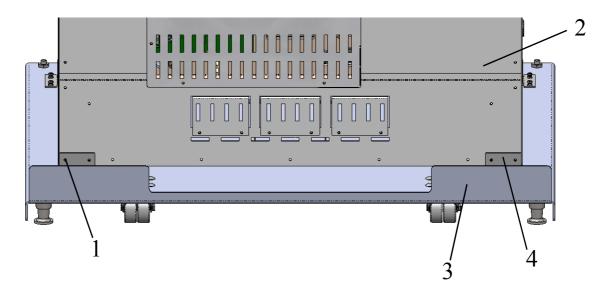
Fissaggio dell'unità sul basamento alla parete posteriore
